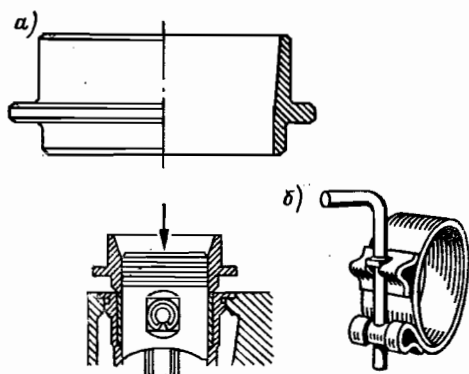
Приспособление для установки поршня с кольцами в цилиндр: *а* — оправка в форме конуса; *б* — ленточная оправка
